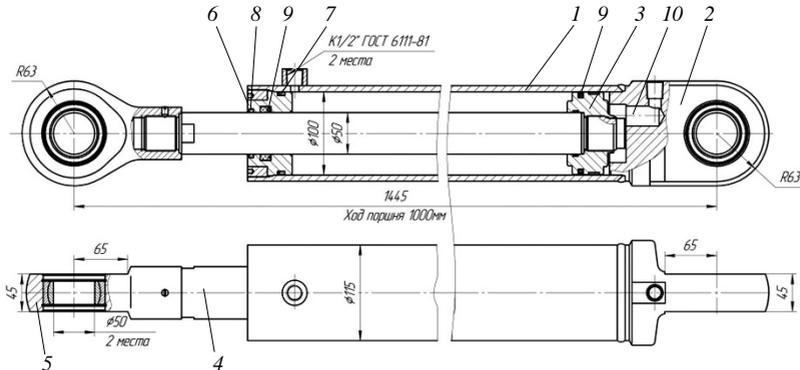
Гидроцилиндр: 1 – корпус; 2 – проушина с шарнирным подшипником; 3 – поршень; 4 – шток; 5 – проушина штока с шарнирным подшипником; 6 – крышка корпуса (букса); 7 – уплотнение статическое; 8 – грязеъемник; 9 – уплотнение динамическое; 10 – демпферное устройство
